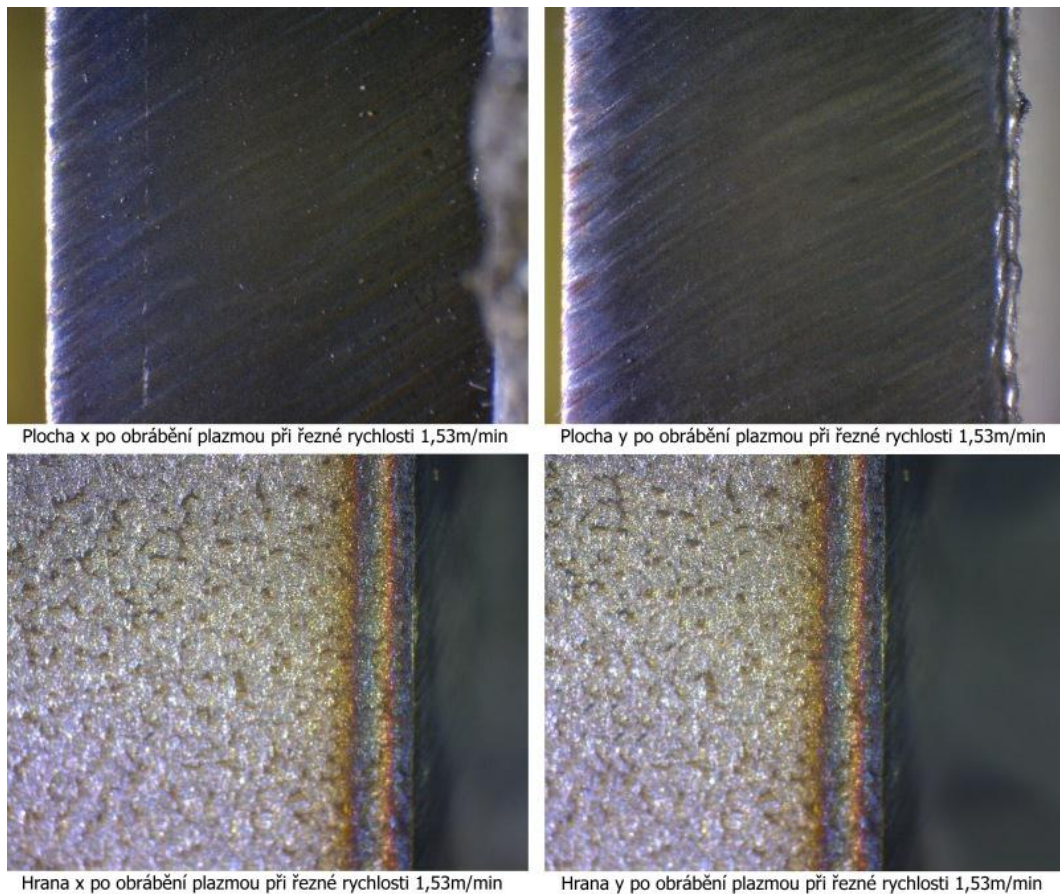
Snímky z mikroskopu vzorku 2 obráběného plazmou - materiál 17 349
